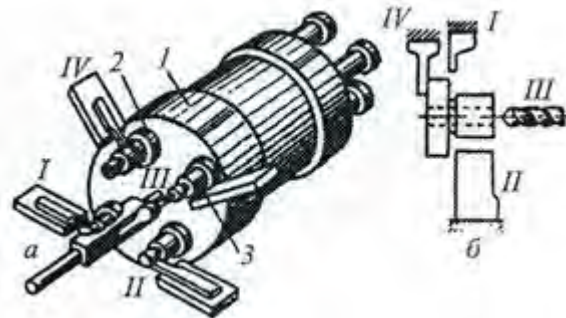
Схема оброблення заготовок на багатшпindelному автоматі
